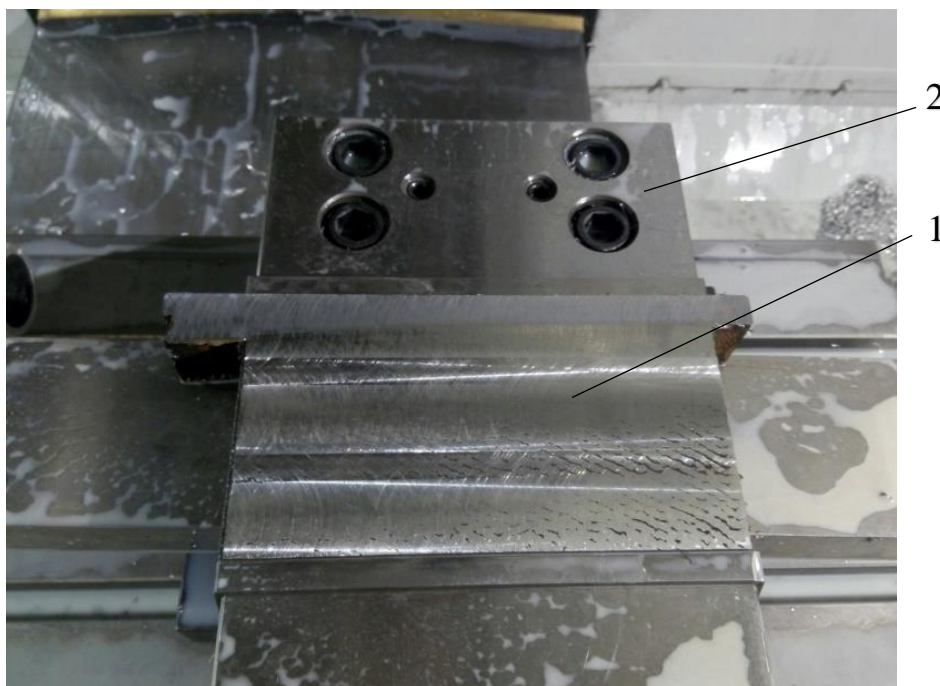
Фотография заготовки из никелевого сплава, установленной в тисках на фрезерном станке. 1 – заготовка; 2 – тиски
